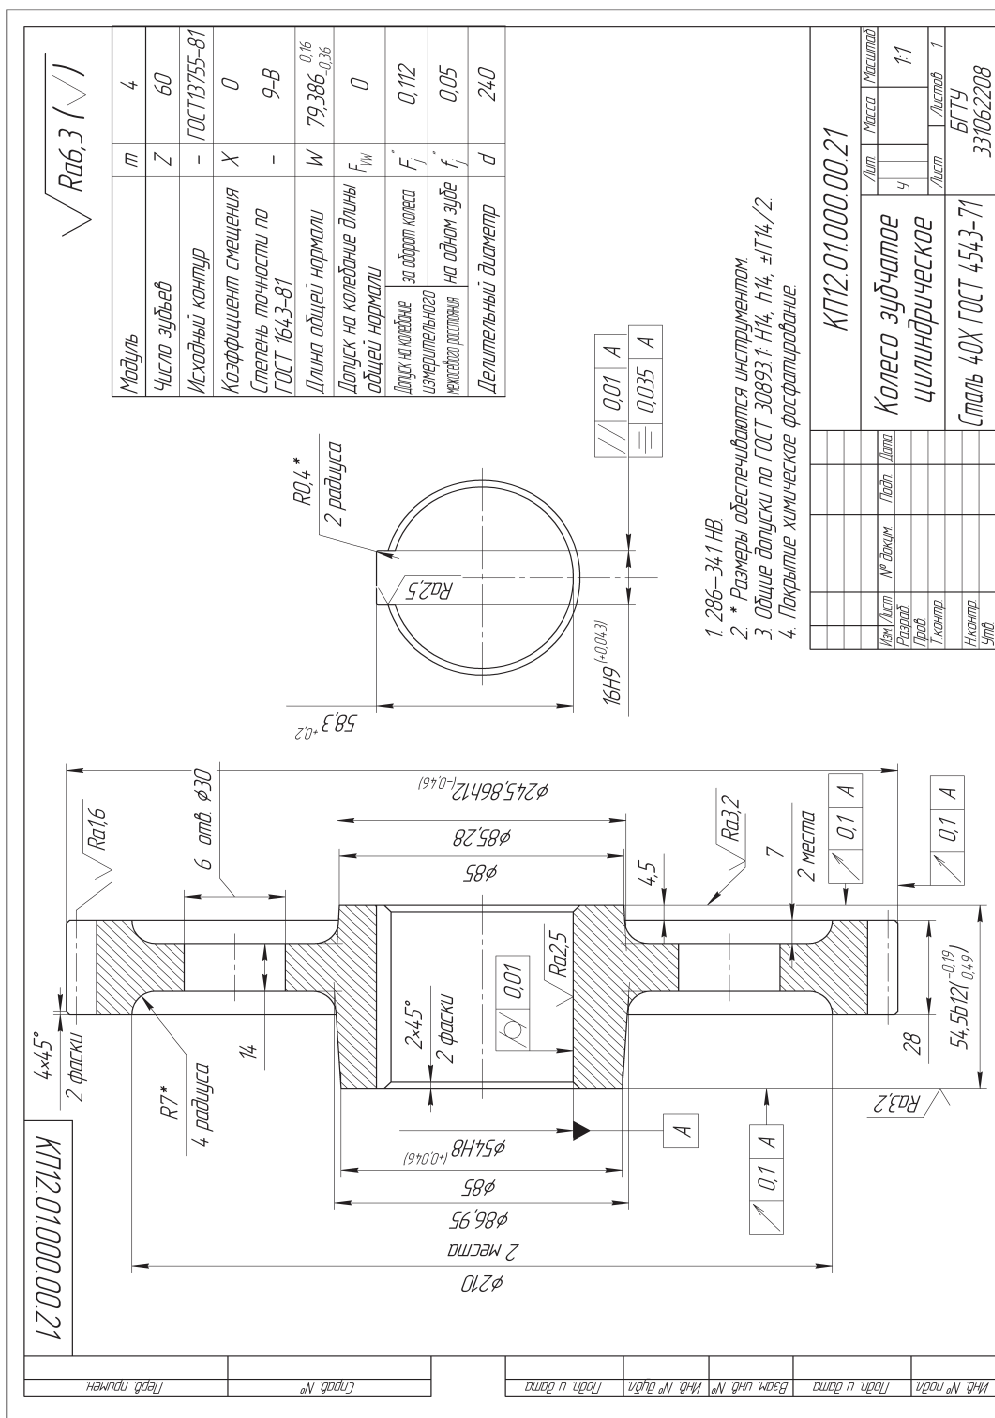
Пример чертежа цилиндрического зубчатого колеса
